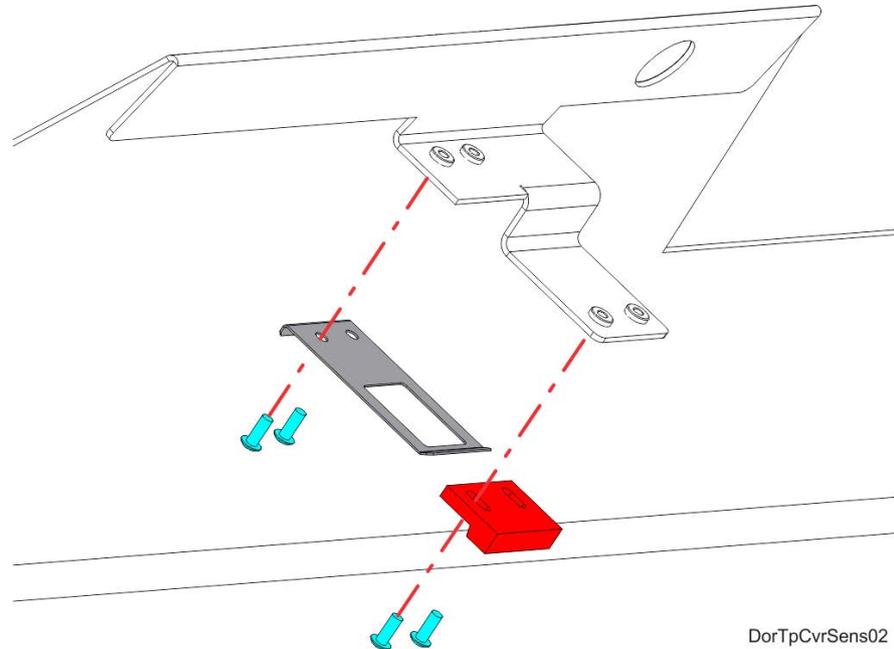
Ubicación de los tornillos de montaje del sensor de la tapa superior
